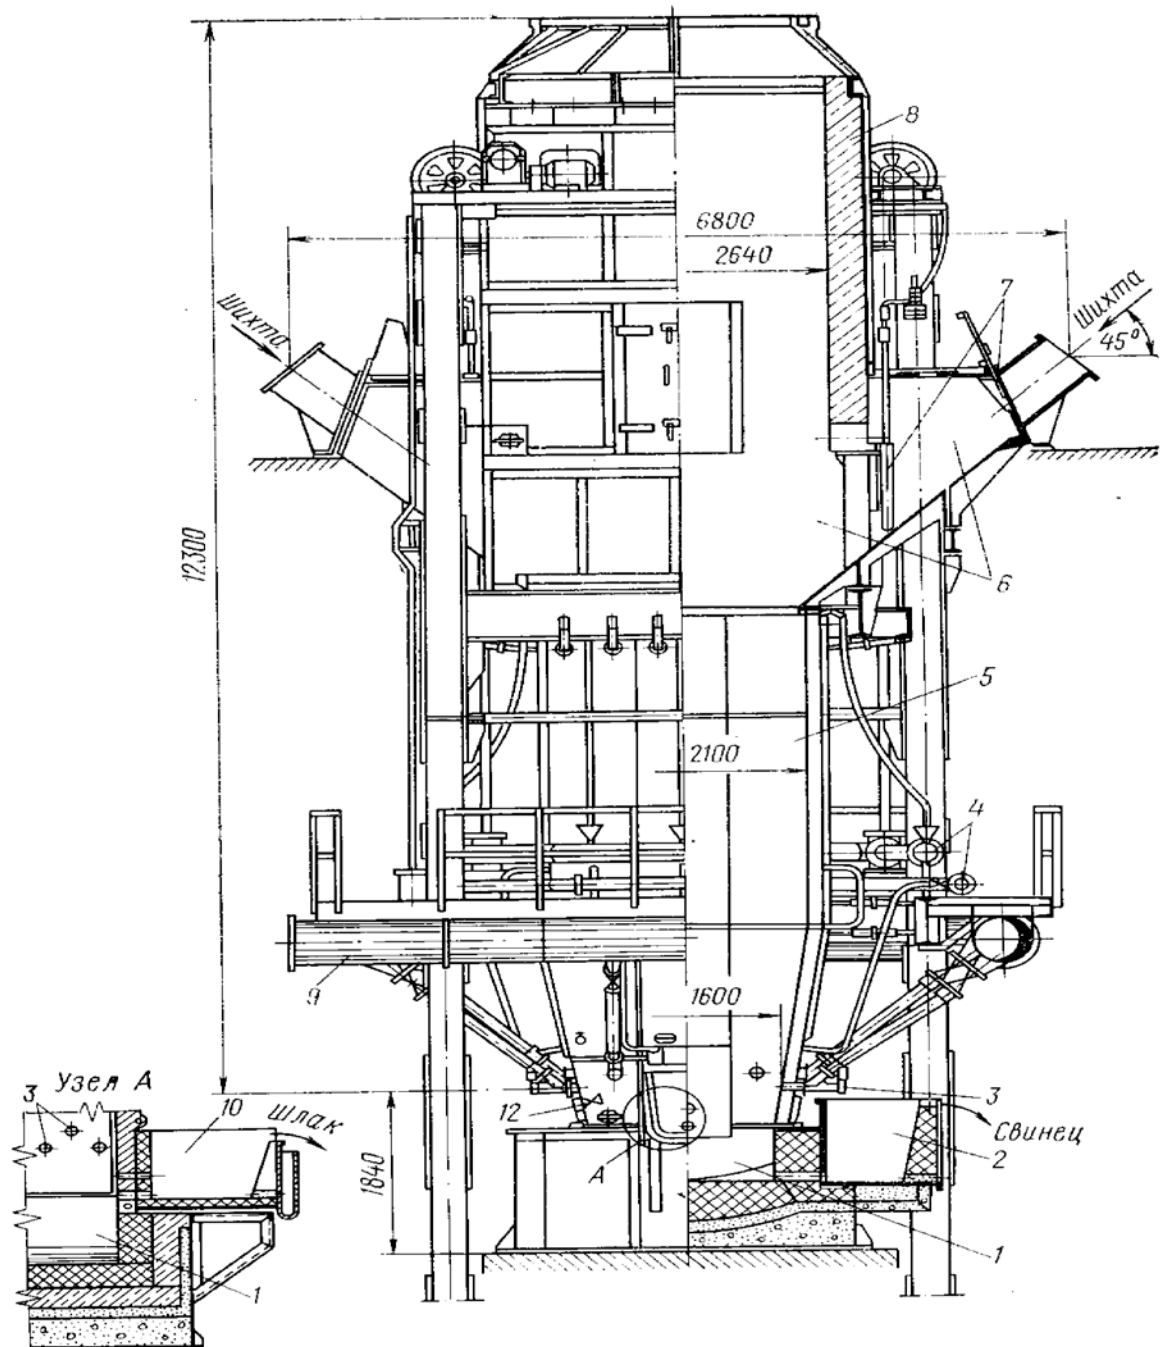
Шахтная печь свинцовой плавки: 1 – горн; 2 – сифон для выпуска чернового свинца; 3 – фурму; 4 – коллекторы системы водяного охлаждения; 5 – шахта печи; 6 – колошник; 7 – загрузочный шибер; 8 – шатер колошника; 9 – коллектор для подвода дутья; 10 – сифон для выпуска шлака
